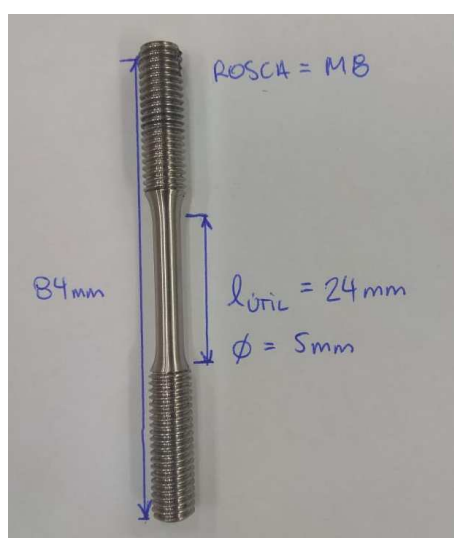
Corpo de prova utilizado para o ensaio de ciclo térmico.
